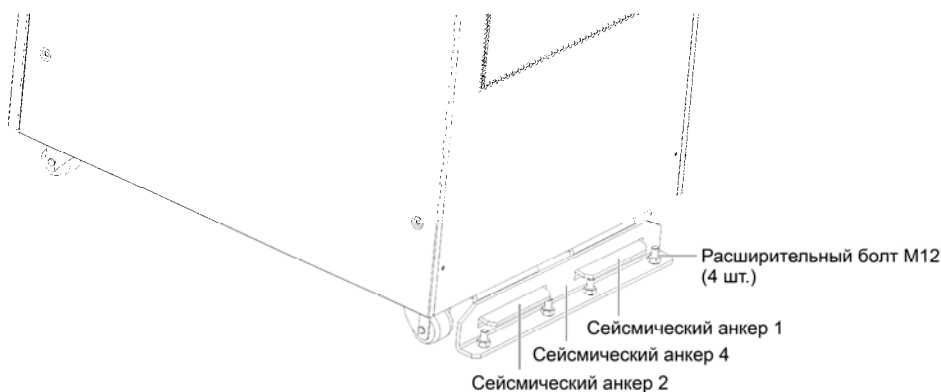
Монтаж дополнительных креплений 4 на полу и крепление шкафа
